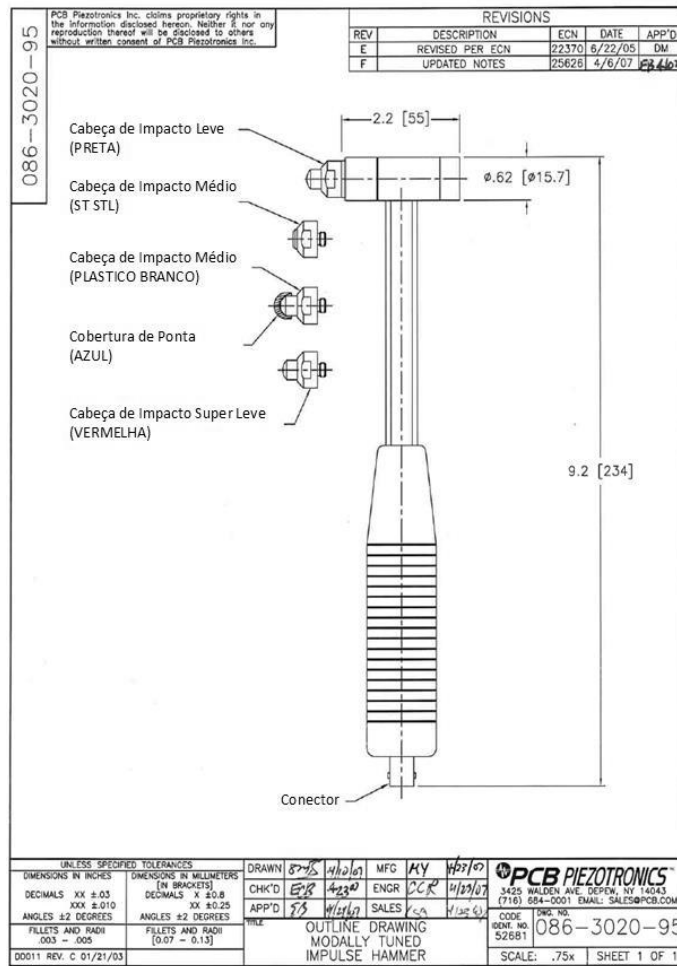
Layout de dimensional do martelo PCB MOD.ICP 086C03 - Fonte original - www.pcb.com
